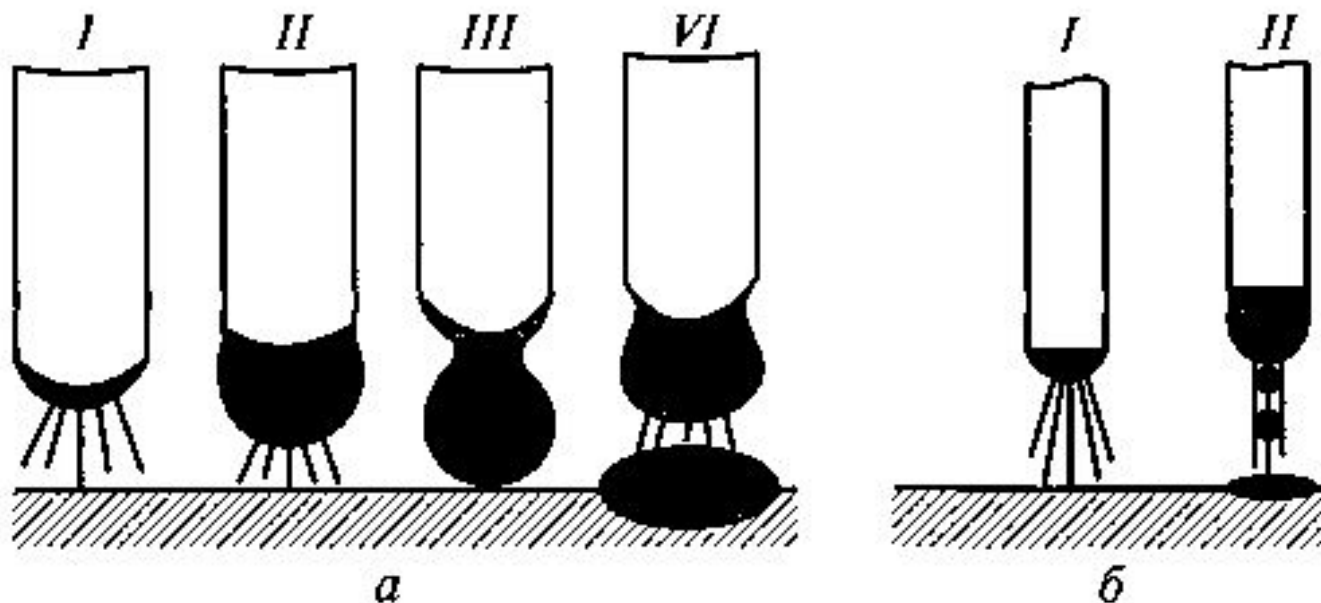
Схемы процессов переноса электродного металла в сварочную ванну:
